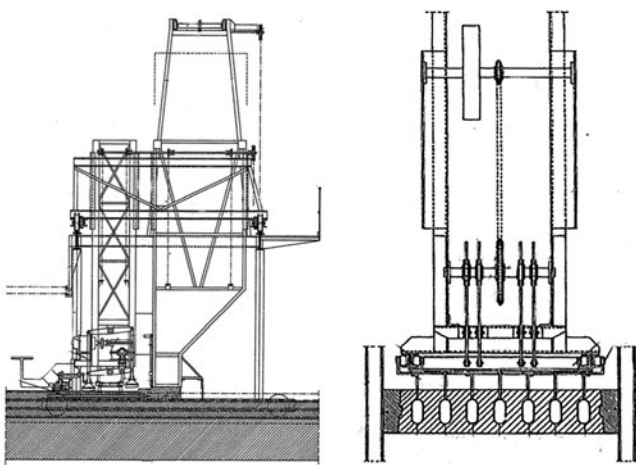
machine de moulage suspendue dans un cadre de portail mobile, inventée par William Schäfer [14].
